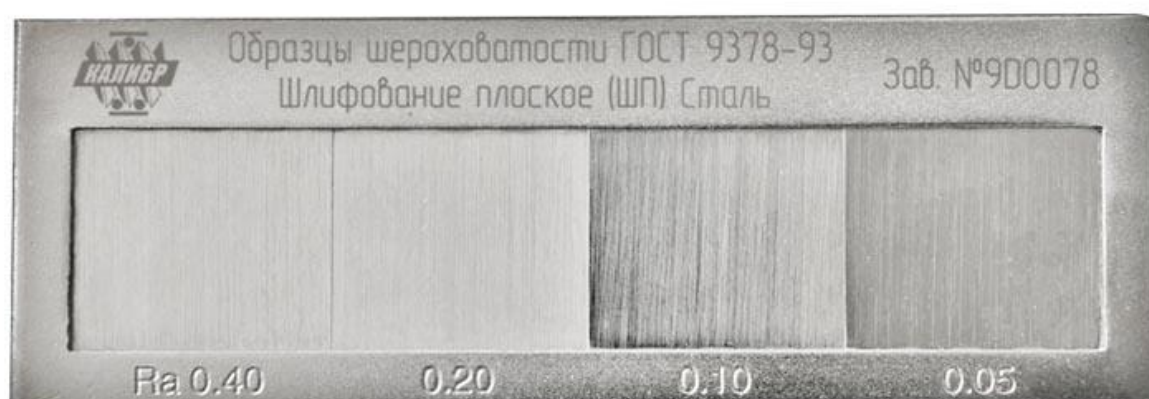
Общий вид образцов шероховатости в наборе из 4 штук в неразборной обойме
